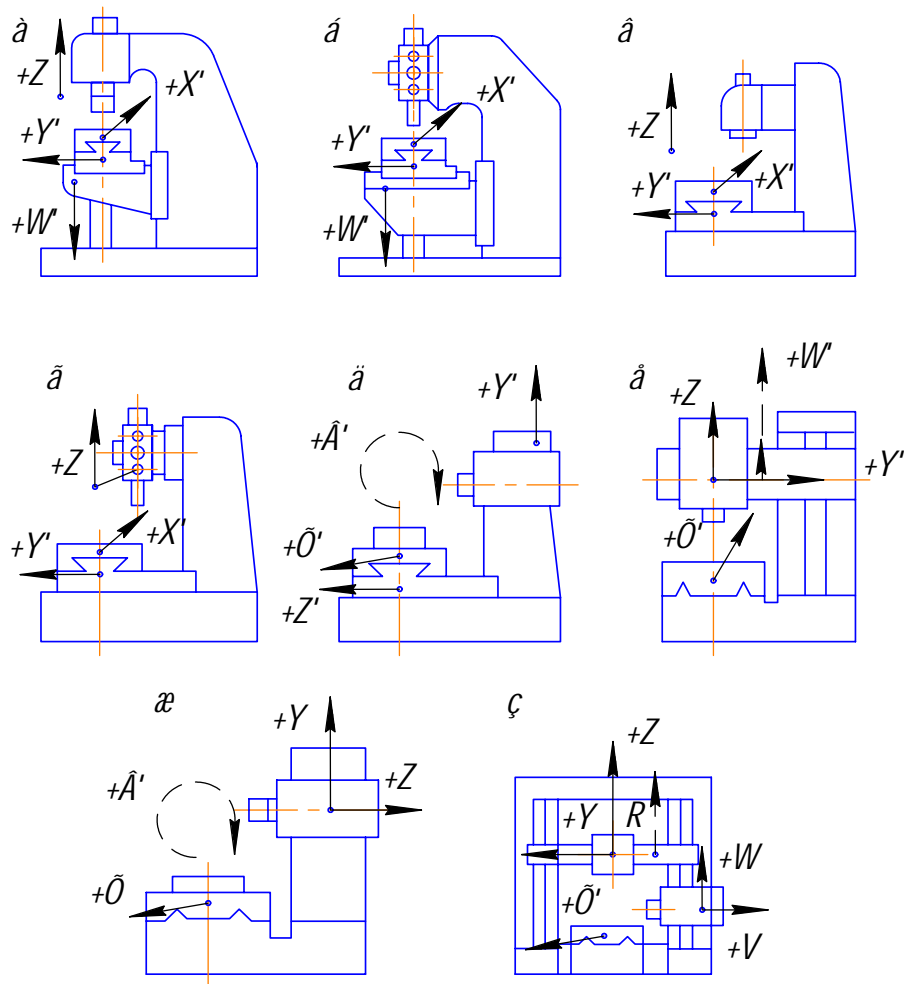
Компоновки фрезерних верстатів з ЧПК:
